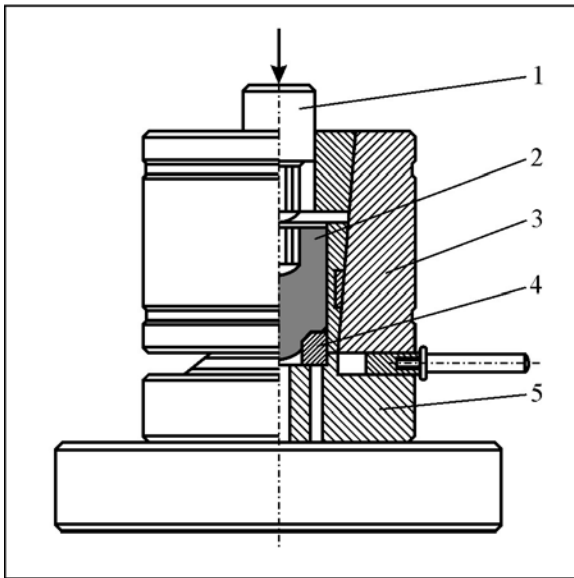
Штамп для видавлювання порожнини в циліндричному штамповому інструменті: 1 – майстер-пуансон; 2 – заготовка; 3 – конічне кільце; 4 – циліндричне кільце-приймач; 5 – нижня плита
